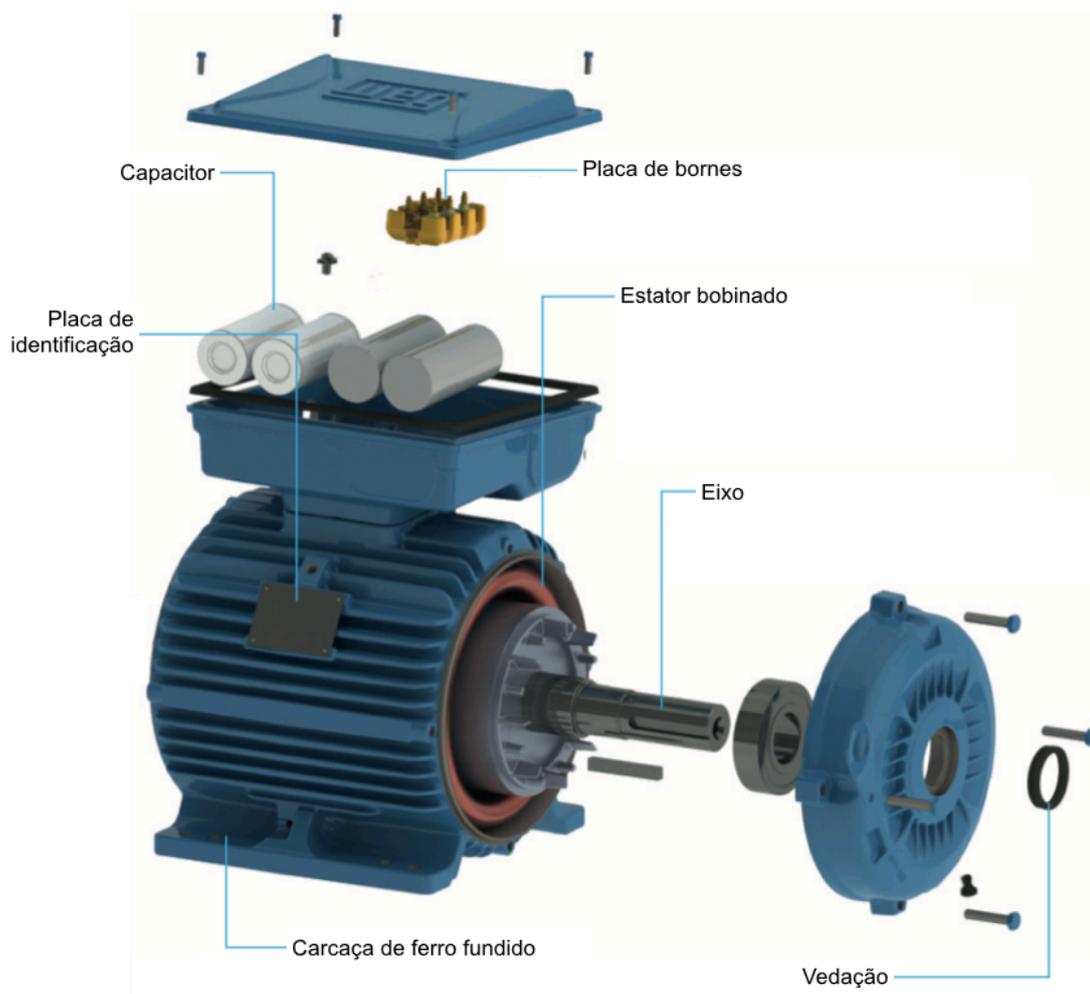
Vista explodida de motor monofásico de fase auxiliar e capacitor de partida.
